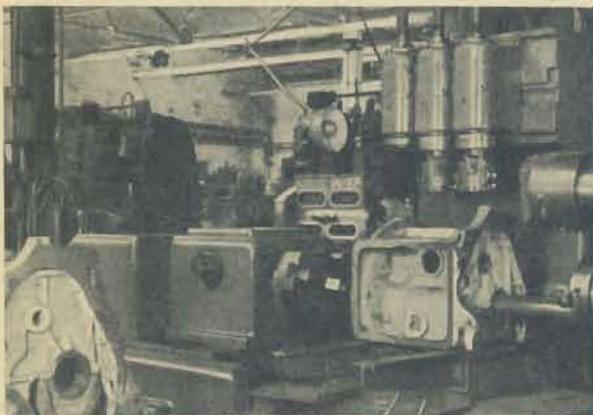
Dreiseitige Feinstbearbeitungsmaschine für Plansseiten-, Kurbelwellen- und Zylinderbohrungen
